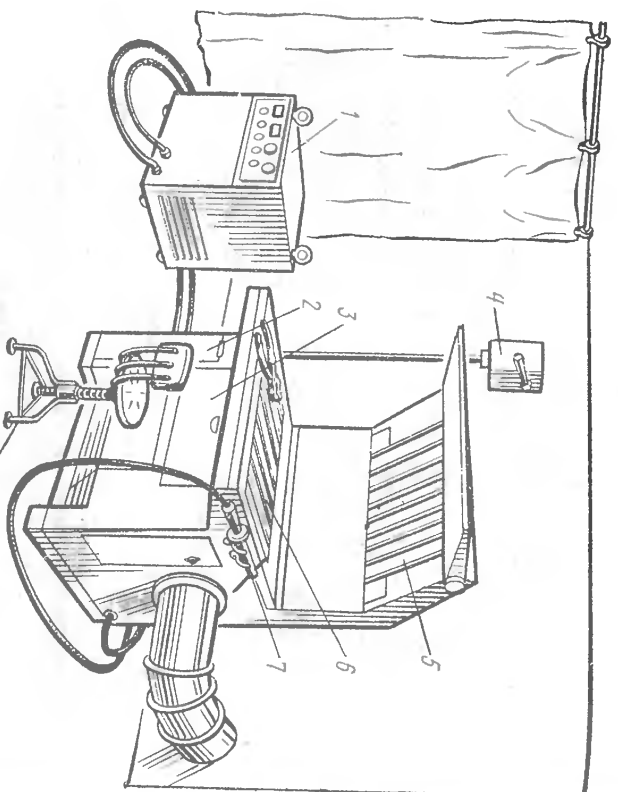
Стационарный сварочный пост ручной дуговой сварки: 1 — источник сварочного тока, 2 — стол для электродов, 3 — ящик для инвентаря, 4 — рубильник, 5, 6 — вытяжная камера, 7 — электрододержатель, 8 — ступь сварщика
